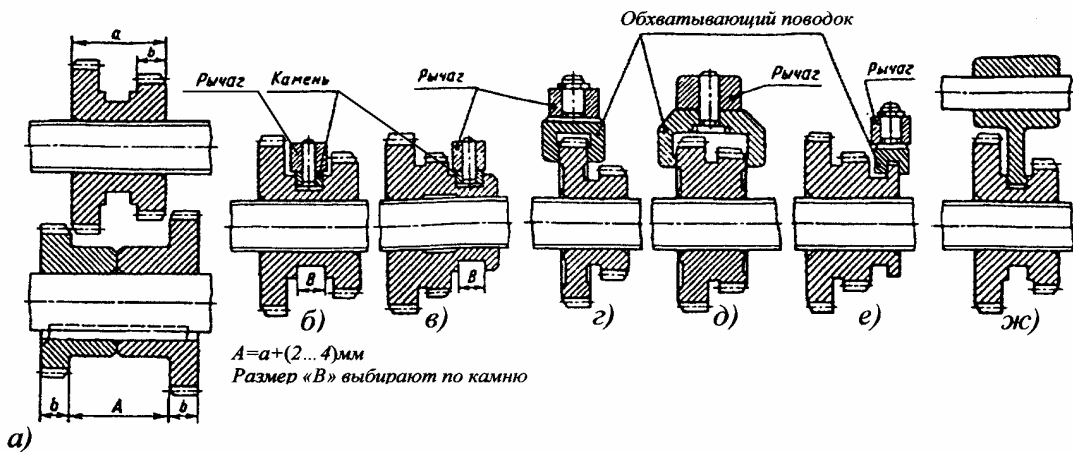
Варианты конструктивного исполнения передвижения скользящих блоков зубчатых колес: б, в - рычагом с камнем; г-е - рычагом с обхватывающим поводком; ж - ползуном с гребнем
